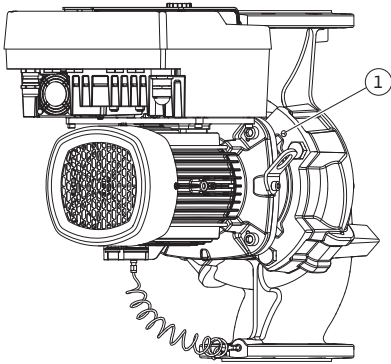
Abdrücken des Einstecksatzes über Gewindebohrungen
